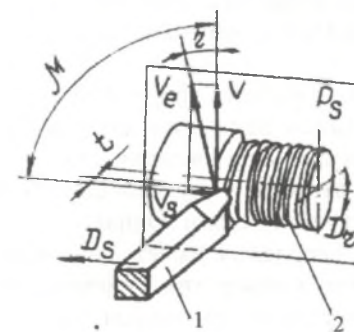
Кинематика продольного точения: 1 – режущий инструмент (резец); 2 – обрабатываемое изделие
